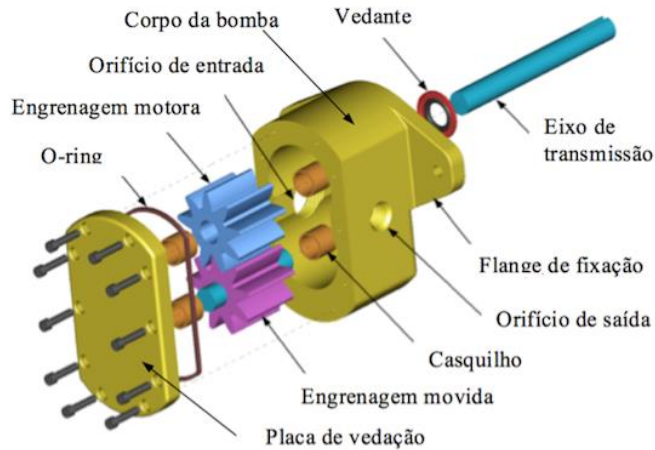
Bomba de carretos/engrenagens em vista explodida. [14]
